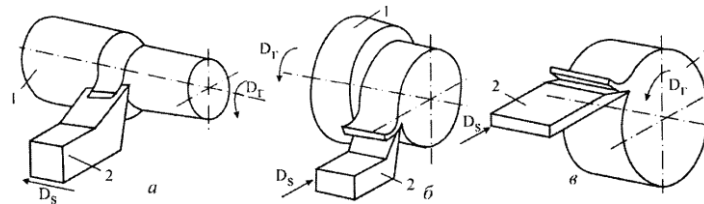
Схеми точіння: а - поздовжнє; б - поперечне радіальне; в - поперечне тангентальне; 1 - заготовка; 2 - токарний різець
